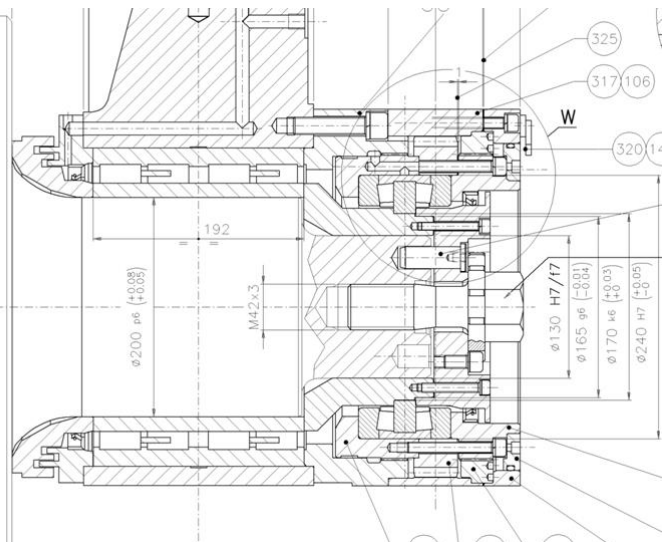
Механізм осьового регулювання верхнього валка безстанинної кліті сортового стану [Manufacturer of High Quality Rollin Mill / AVTAR Foundry & Workshop. – India. - <http://www.rollingmillmachinery.biz/rolling-mill.html>]
